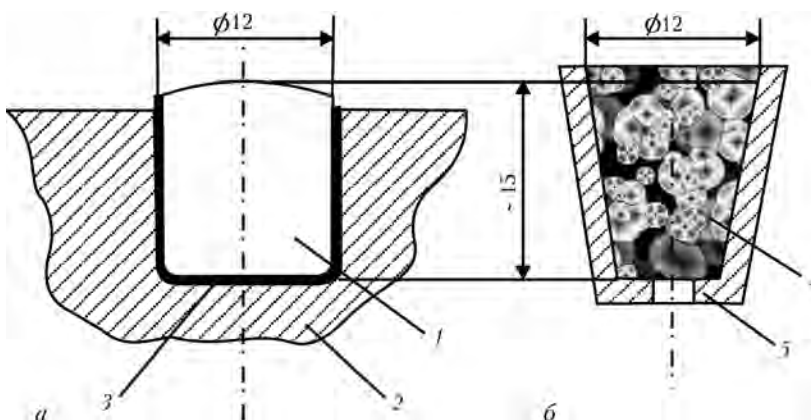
Геометрические параметры отработавших монолитной (а) и дробленой (б) твердосплавных вставок типа В-20 в тигле дериватографа: 1 — твердосплавная вставка; 2 — корпус буровой коронки; 3 — припой Л-63; 4 — дробленая твердосплавная вставка; 5 — корпус тигля дериватографа Q-1500
